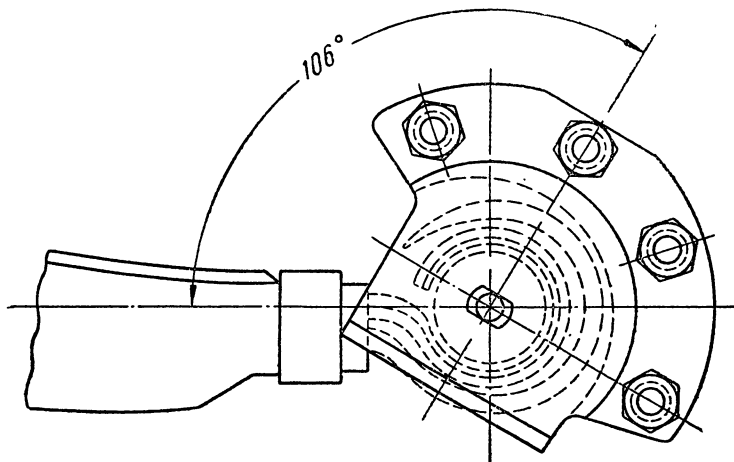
Крепление переднего конца передней рессоры автомобиля М-72:
